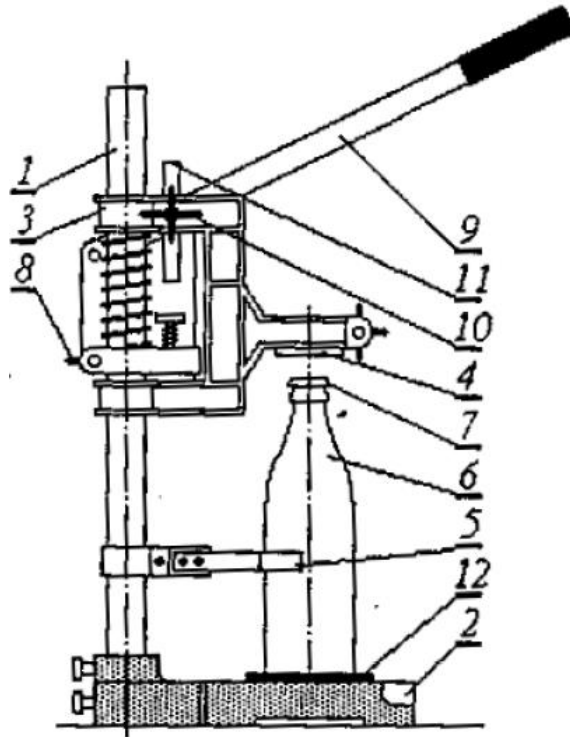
Ручний пристрій закупорювання пляшок кронен-пробками: 1 – стійка; 2 – основу; 3 – механізм вертикального переміщення; 4 – закупорювальна голівка; 5 – напрямна; 6 – пляшка; 7 – кронен-пробка; 8 – регулювальний гвинт; 9 – важіль; 10 – стопорний гвинт; 11 – регульований упор; 12 – гумова пластина
